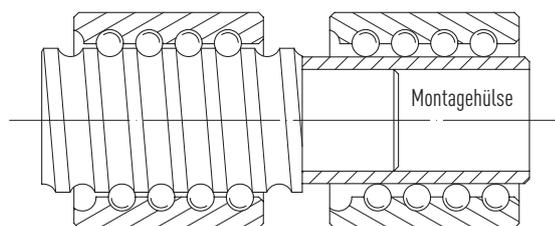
Abzug der Mutter von der Spindel mit Hilfe der Montagehülse
